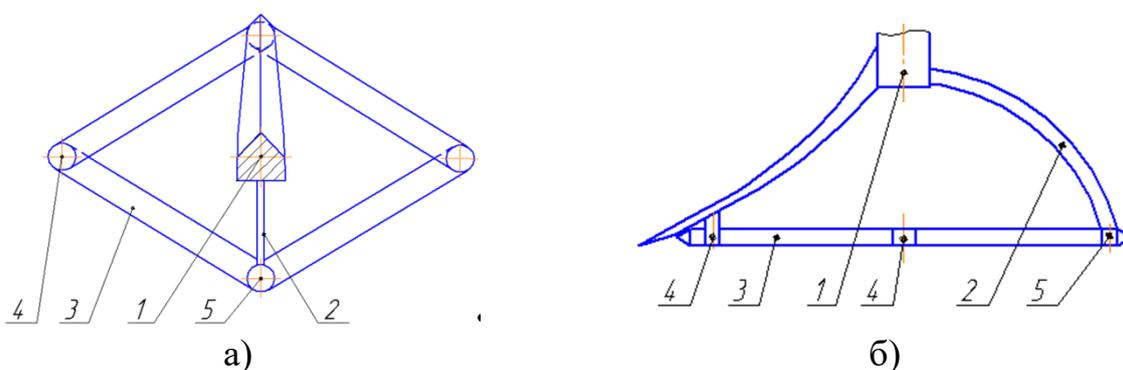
Схема плоскорежущего рабочего органа для засорённых камнями почв: а) – вид сверху, б) – вид сбоку, обозначения в тексте
